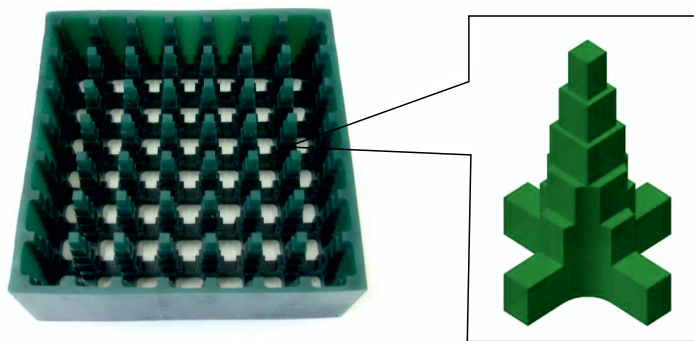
Гребенчатый фильтр, изготовленный из ювелирного воска с помощью фрезерного станка с ЧПУ
